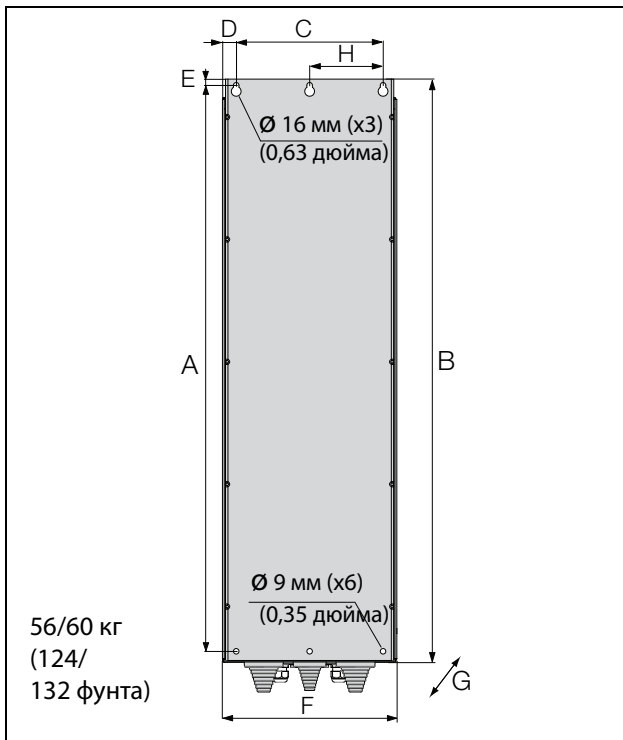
Устройство Emotron FDU моделей с 48-090 по 175 (размер корпуса E).
